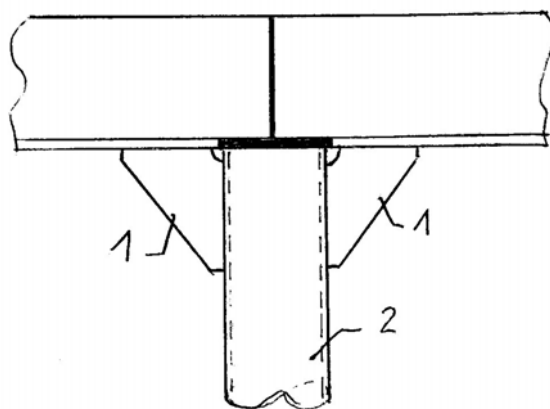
Konstrukcja w rejonie górnego końca pilersa
